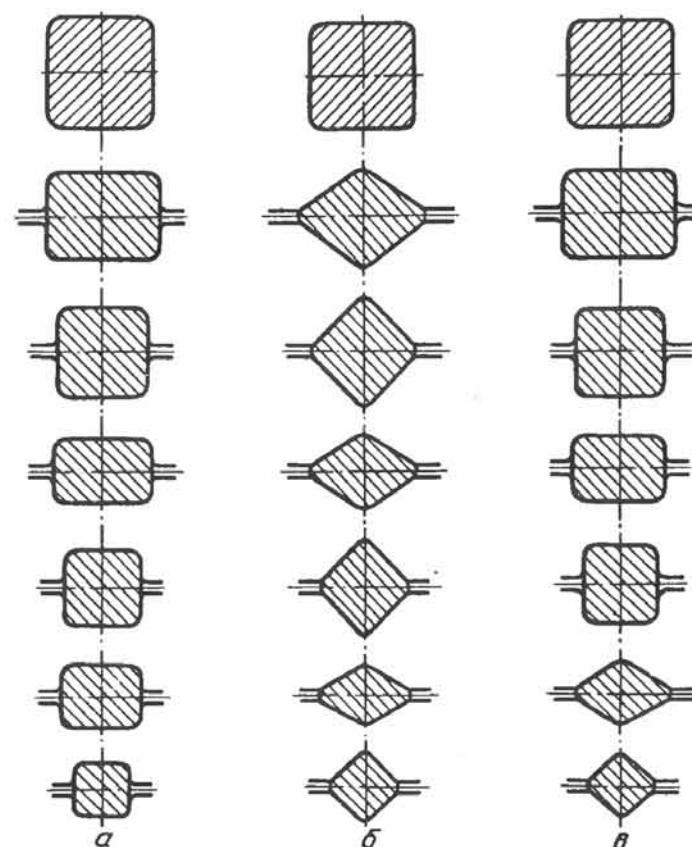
Схемы калибровок непрерывных заготовочных станов:
